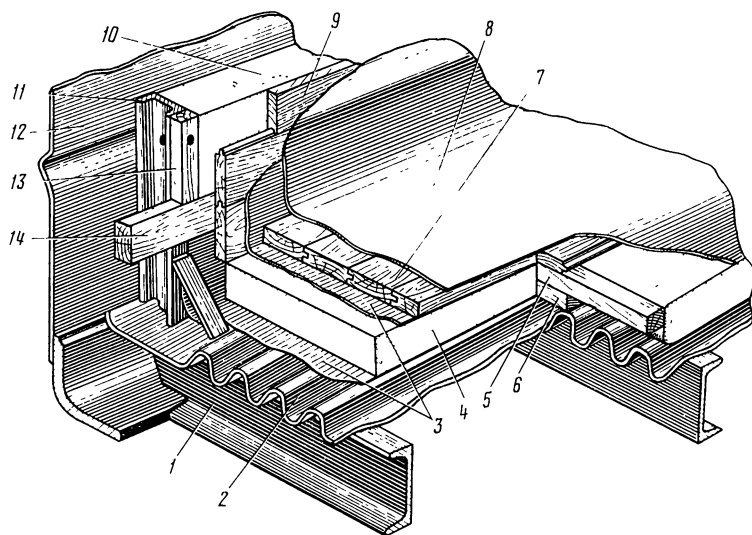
Устройство пола и стены вагона-ледника конструкции 1948 г.:
